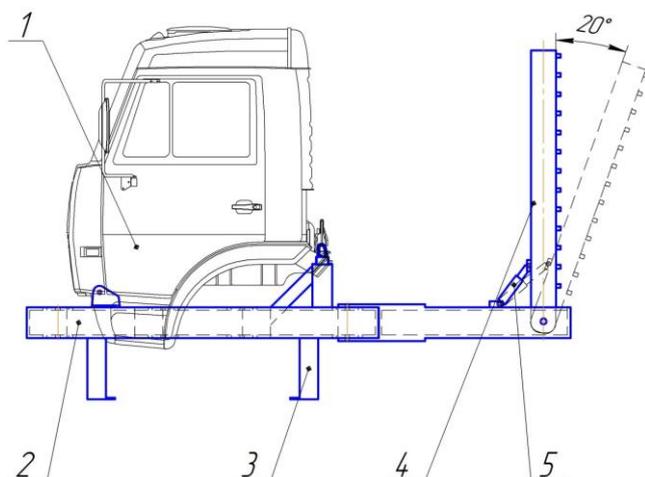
Разрабатываемый стапель для правки кабин грузовых автомобилей: 1-кабина ремонтируемого автомобиля; 2-платформа; 3-ножка; 4-силовая стойка; 5-гидроцилиндр (пневмоцилиндр).
